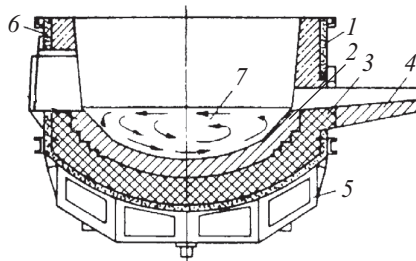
Схема дуговой печи с индукционным перемешивающим устройством: 1 – стеновые блоки; 2 – подина; 3 – футеровка; 4 – футеровка желоба; 5 – статор; 6 – изоляционный слой; 7 – направление движение металла
